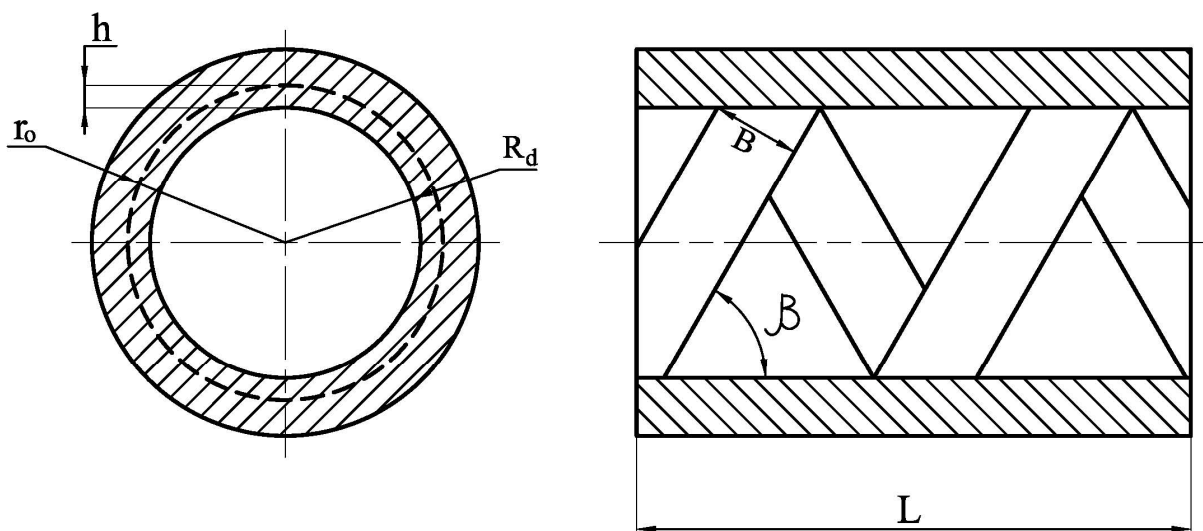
Схема контакта обрабатываемой заготовки с инструментом
